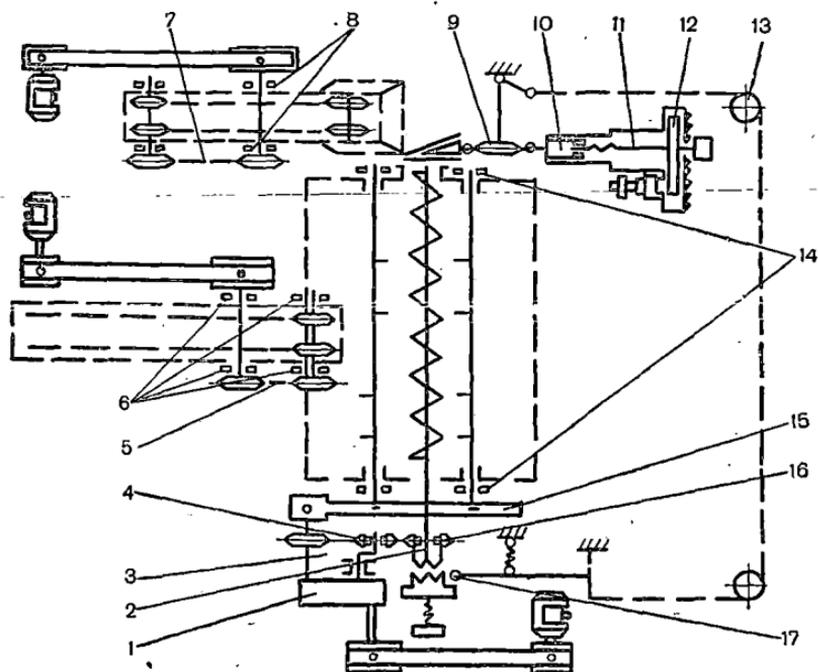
Схема смазки агрегата АПС-6 (смесителя С-7):
